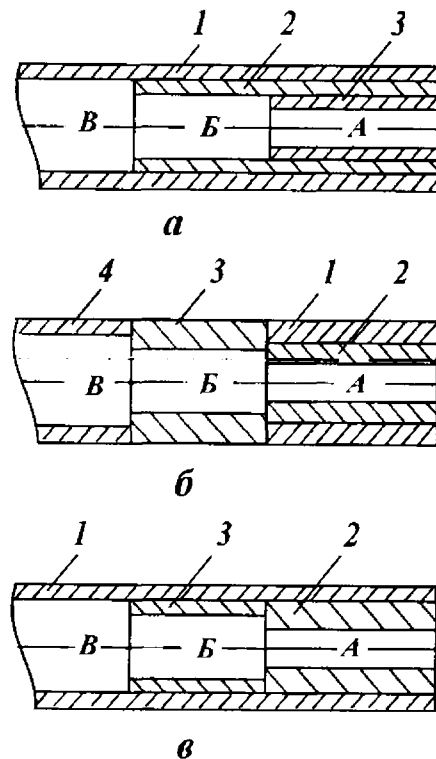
Схемы обтачивания ступенчатого вала: 1 – 4 номера переходов; А, Б, В – ступени вала
